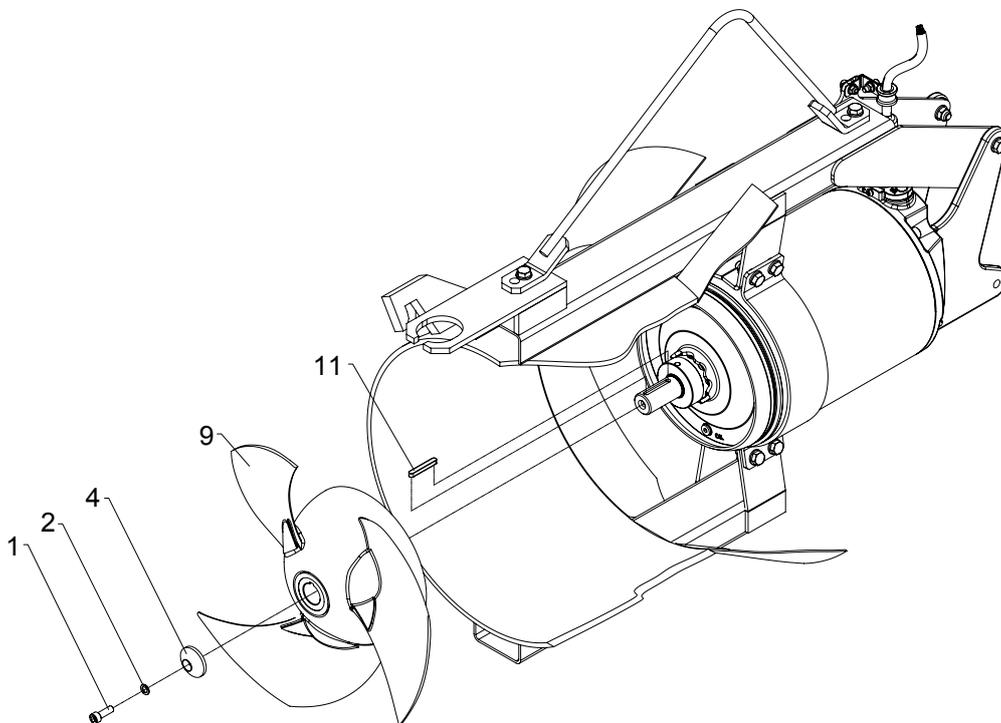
Разборка / сборка пропеллера, XRCP 400/500
